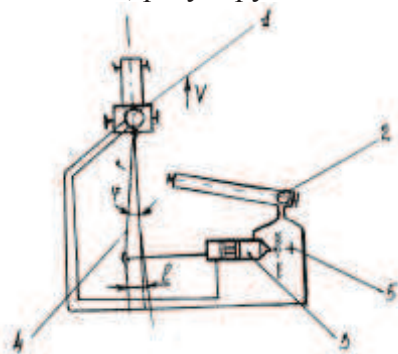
Схема системы автоматического управления движением жатки с боковой навеской
